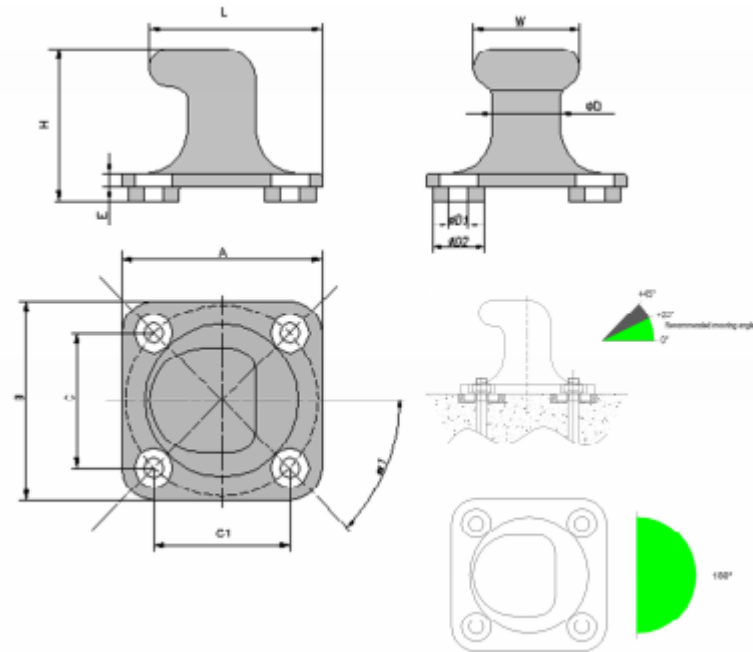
Definición geométrica del bolardo. (Fuente: www.prosertek.com).
